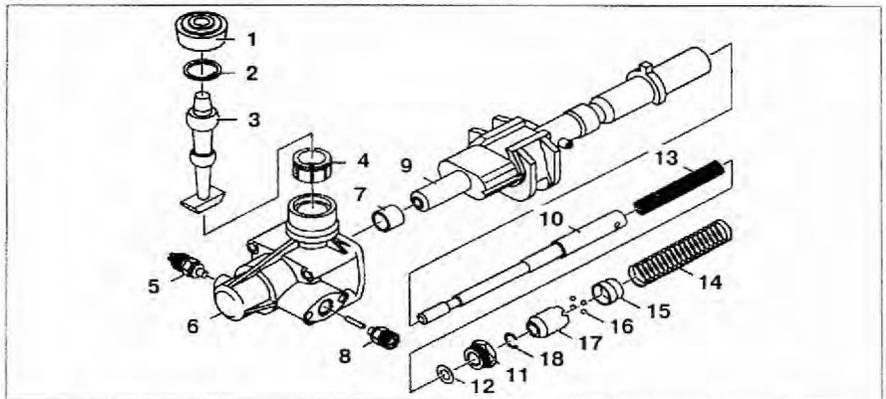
Разборка и сборка механизма переключения передач: 1 – Резиновый чехол; 2, 18 – Стопорные кольца; 3 – Рычаг переключения; 4 – Подшипник; 5 – Датчик нейтрального положения; 6 – Корпус механизма переключения передач; 7 – Втулка; 8 – Выключатель фонарей заднего хода; 9 – Труба переключения; 10 – Тяга переключения; 11 – Болт; 12 – Прокладка; 13, 14 – Пружины; 15, 17 – Стопорные втулки; 16 – Шарики.
